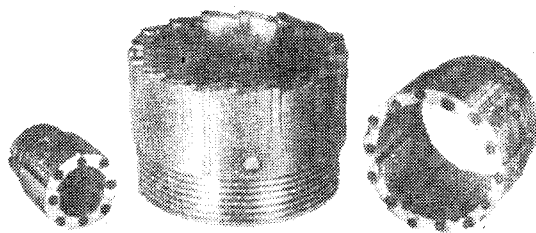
Кольцевые коронки, армированные твердосплавными пластинками
